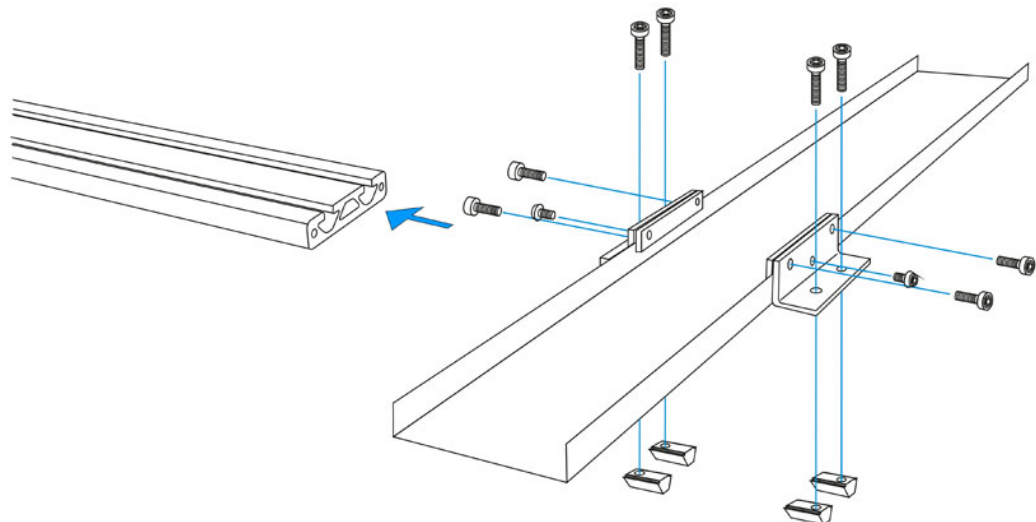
Fixation de chenal posée librement sur la barre profilée
